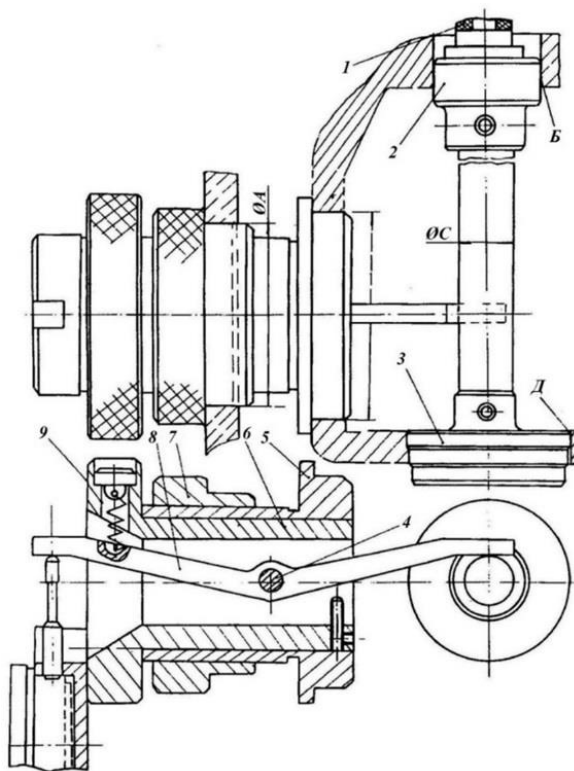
Приспособление для контроля смещения пересекающихся осей в картере редуктора
